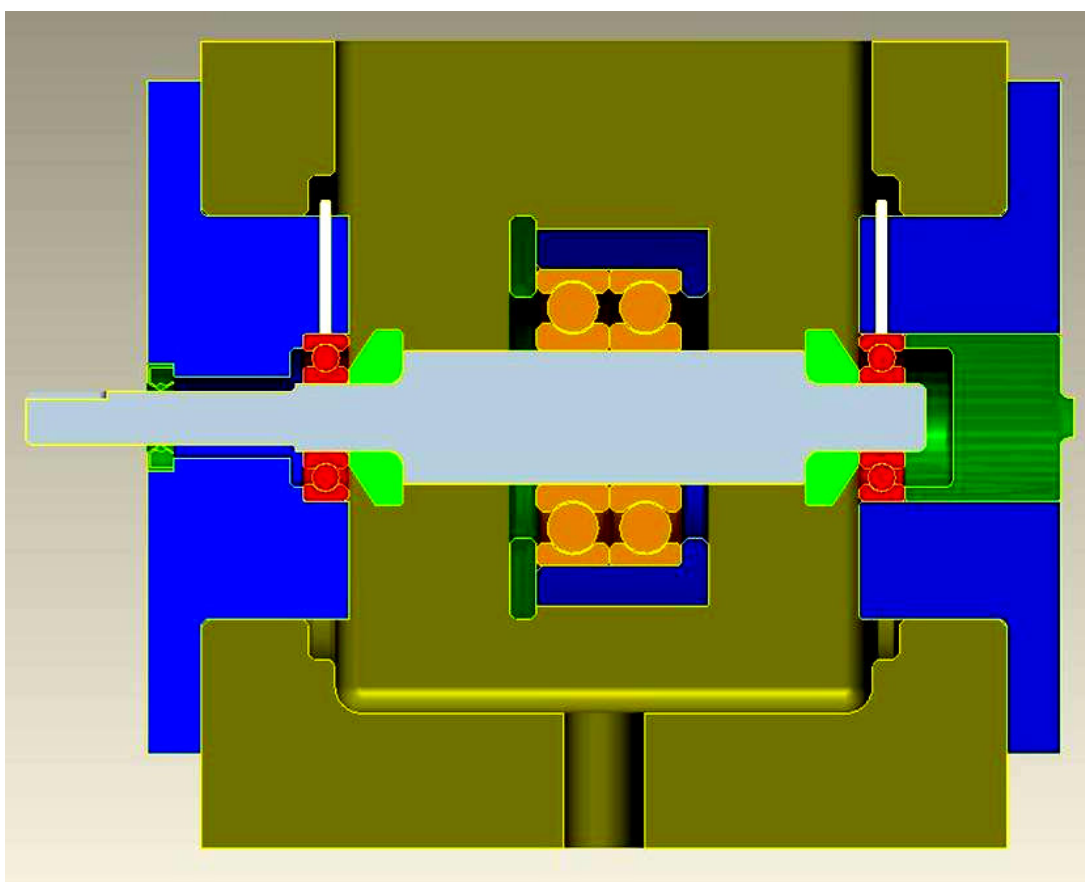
Desenho em corte longitudinal do aparato utilizado para teste dos rolamentos.
